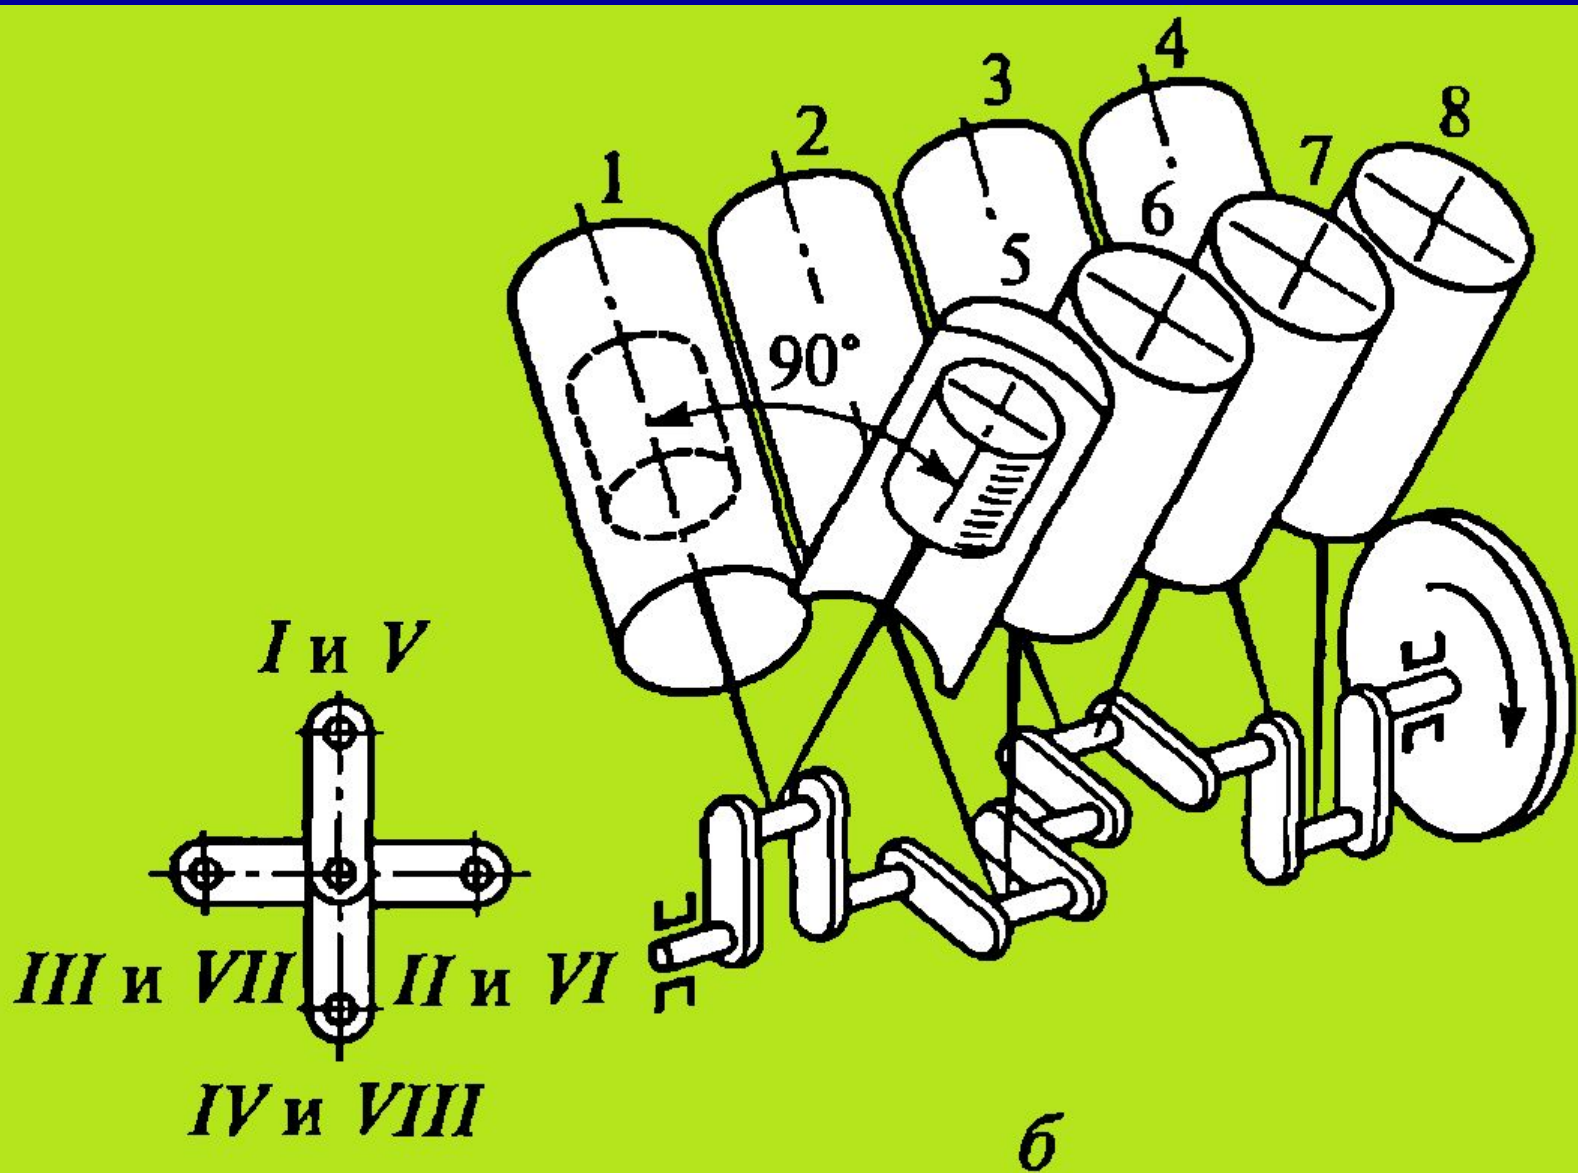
,б. Схема кривошипно-шатунного механизма четырехтактного восьмицилиндрового V-образного двигателя.
